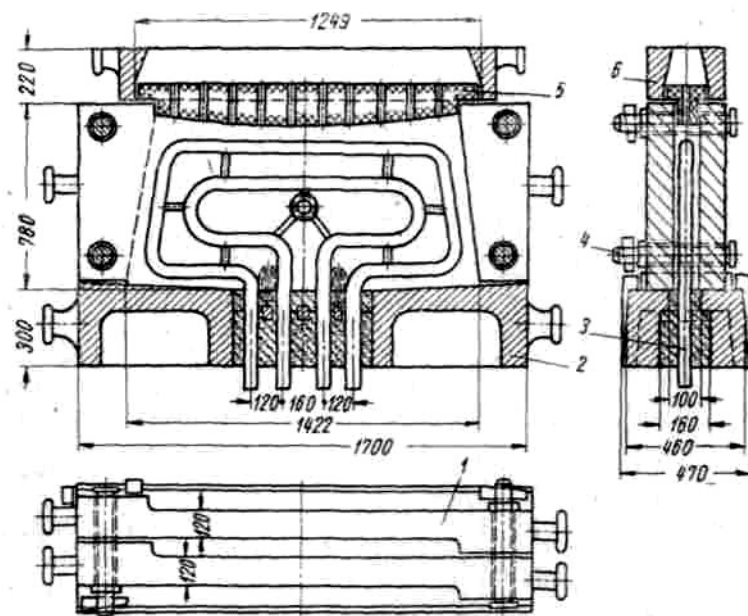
Форма для отливки шахтного холодильника увеличенных размеров
